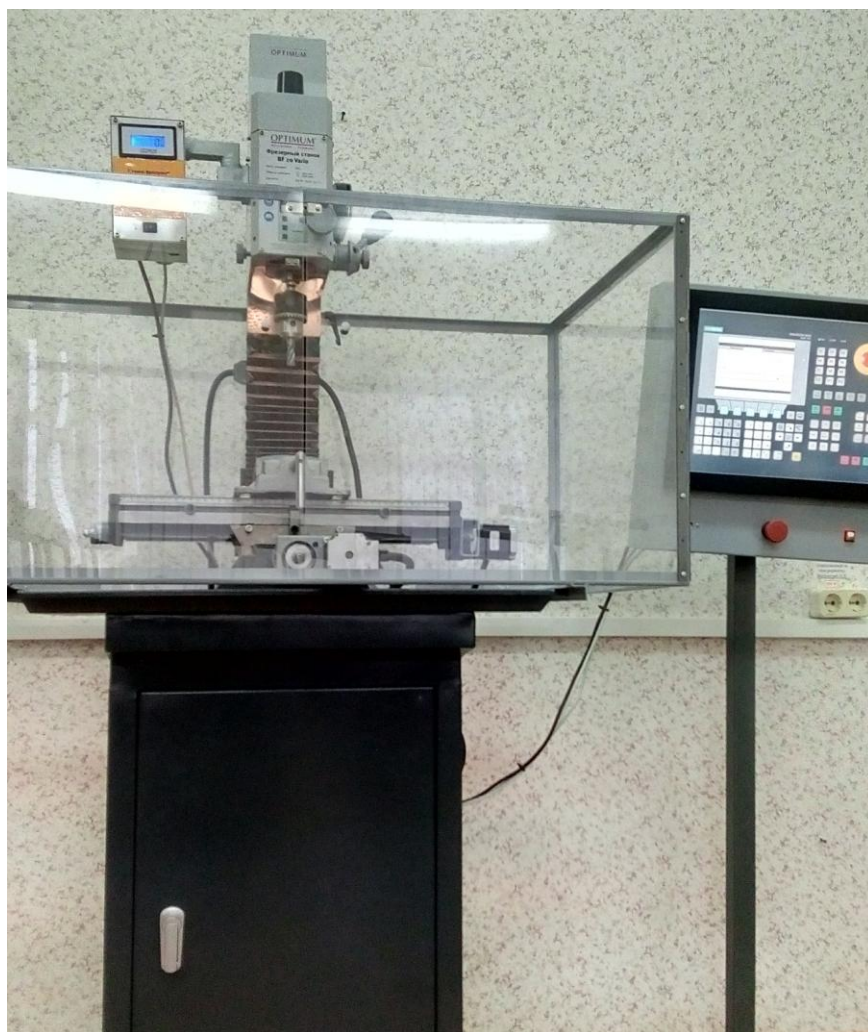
Фрезерный станок с ЧПУ Омега Ф3Ф-ВФ20
